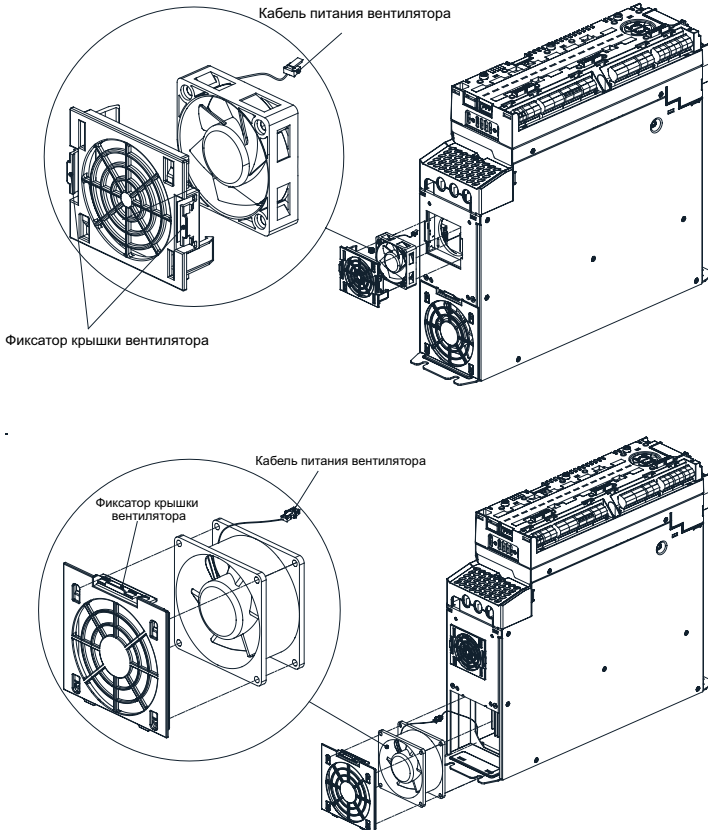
Замена вентилятора инверторного блока типоразмера Н1...Н3
